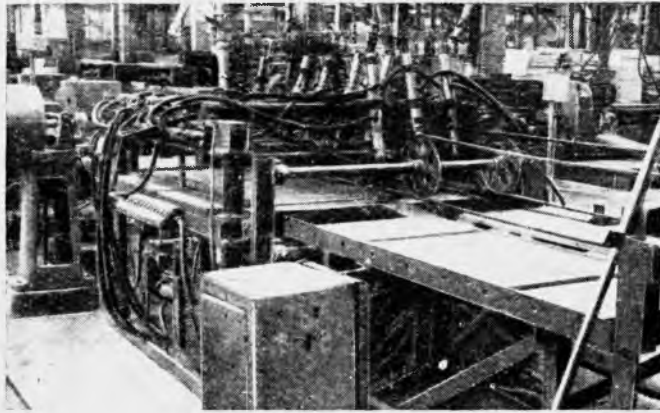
16-шпиндельный сверлильный агрегат, для присадки отверстий в щитах
